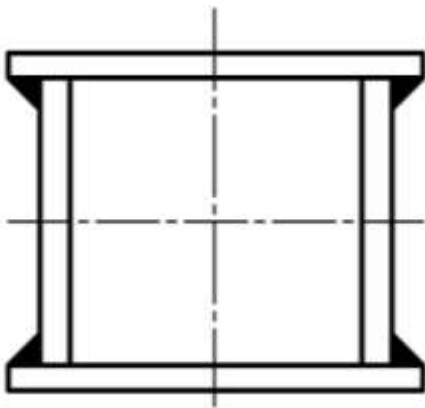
Разработать принципиальную схему базирования деталей и приспособлений для сборки и сварки рамных конструкций
